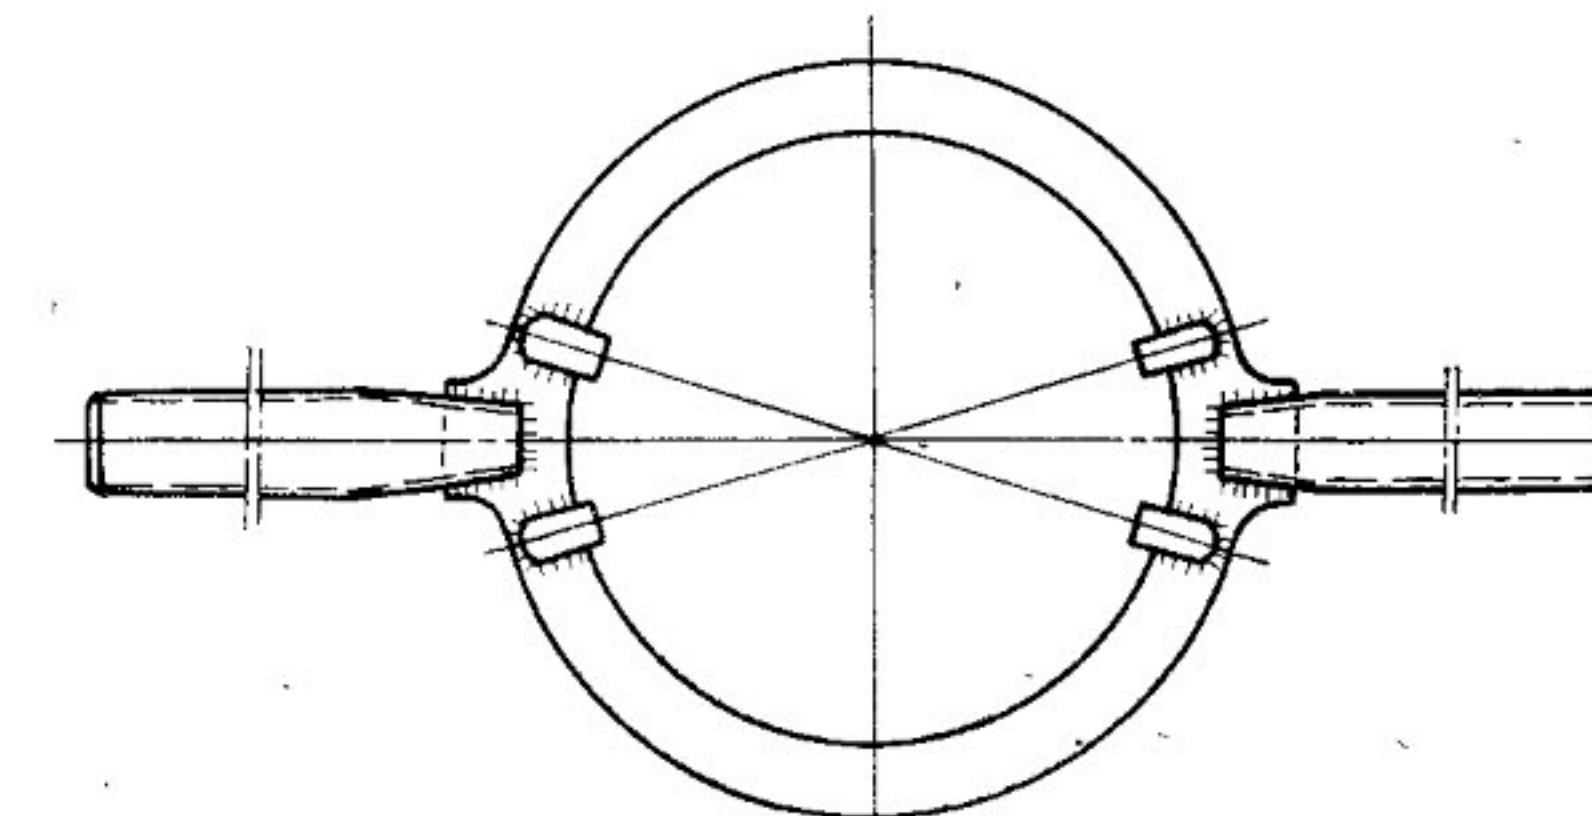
Ключ для предварительной затяжки гайки втулки несущего винта
